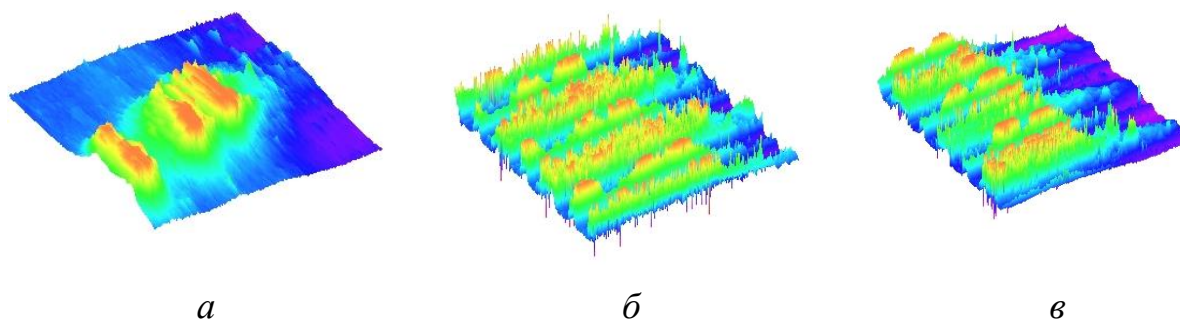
Общий вид 3D-изображения поверхности структуры для оценки шероховатости на образцах, полученных режущим (*а*), деформирующим (*б*) и режуще-деформирующим (*в*) метчиками
